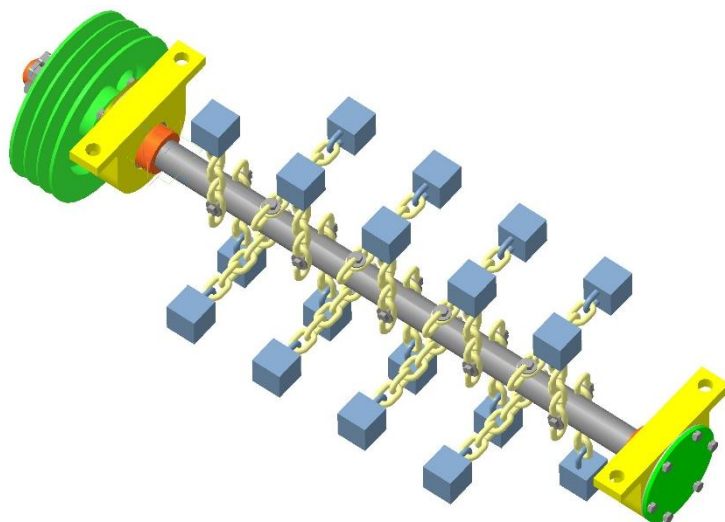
Ударный рабочий орган льдоскалывателя, оборудованный бойками с кубической ударной поверхностью на гибкой связи
